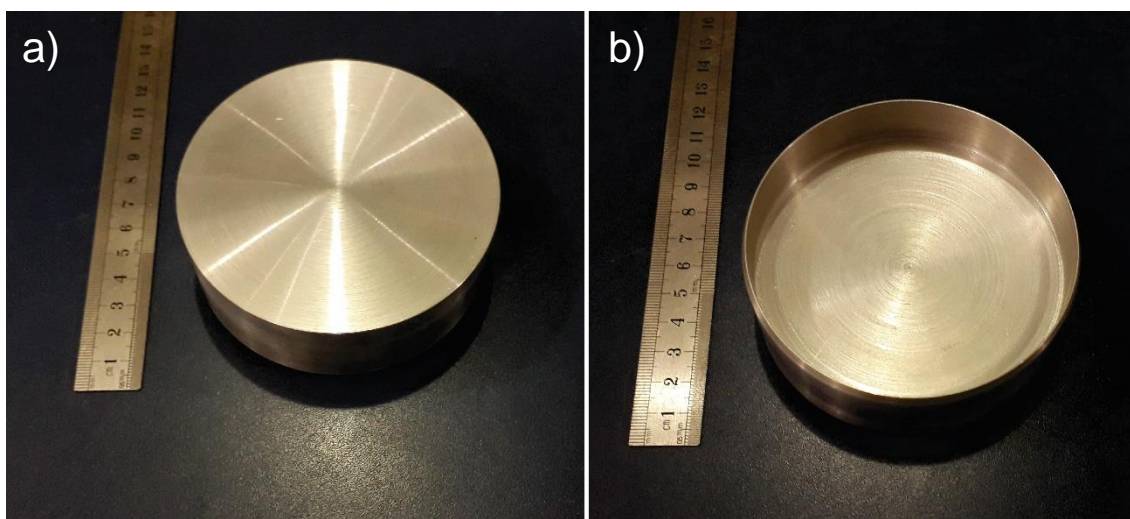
Modelo logo após a fabricação: a) Vista da parte de cima b) vista da parte de baixo.
